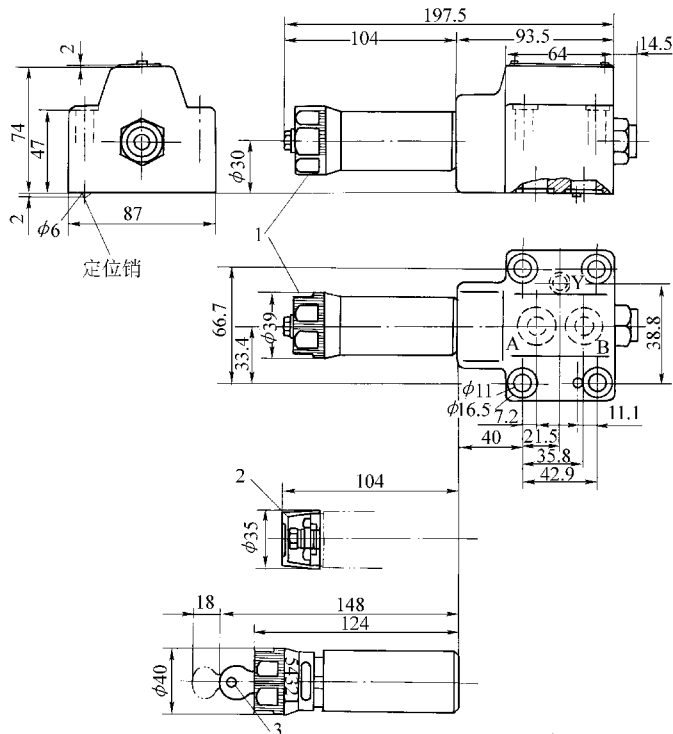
DZ10DP 型直动式顺序阀外形尺寸
